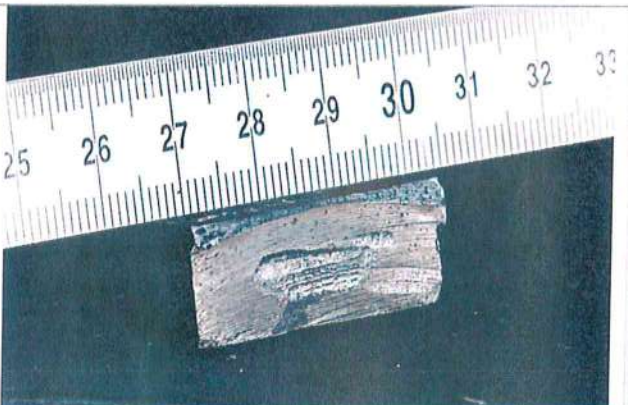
LARGHEZZA DEL CAMPIONE
